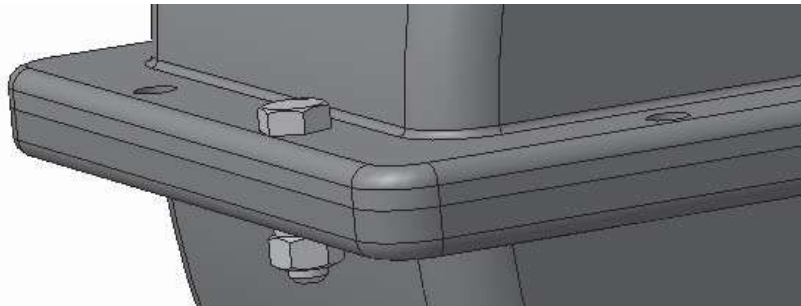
Болтове з'єднання фланців корпуса і кришки
